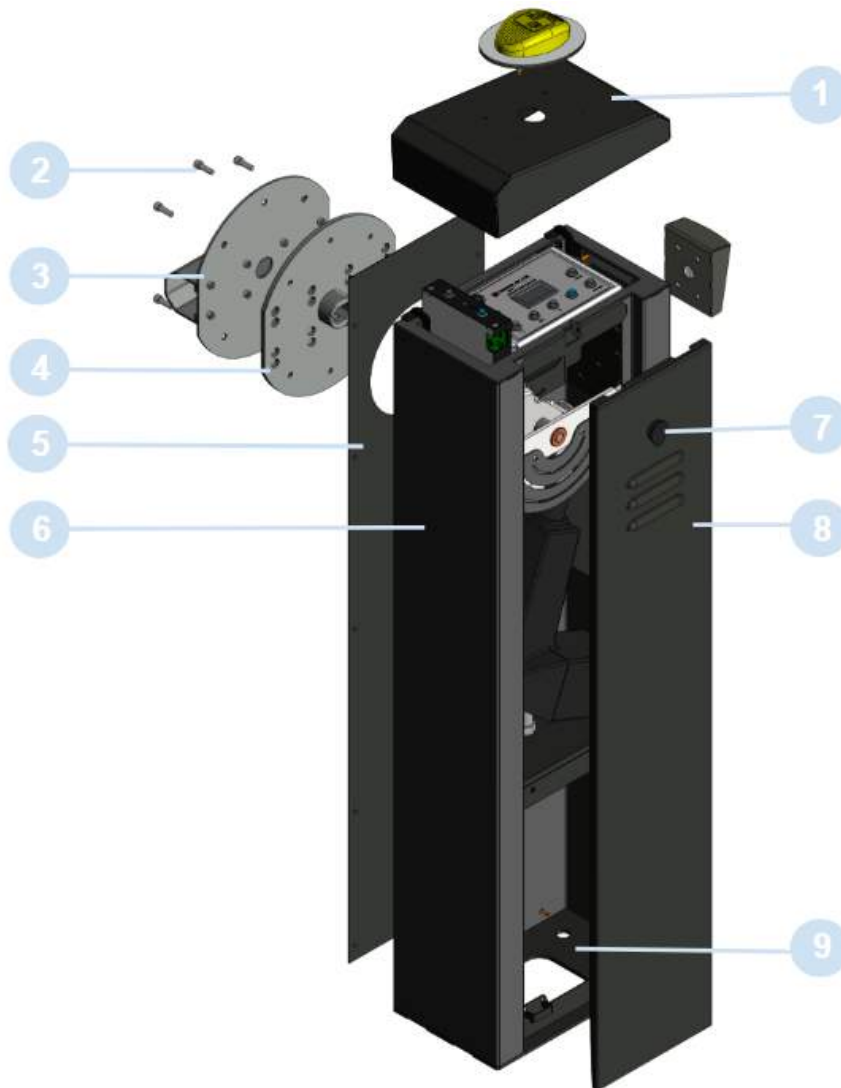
Внешний вид и состав корпуса шлагбаума
